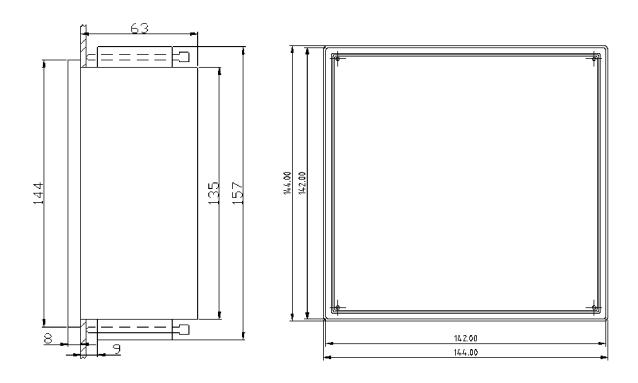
Габаритные размеры щитового варианта указателя положения РПН УП23 (типоразмер Б).
